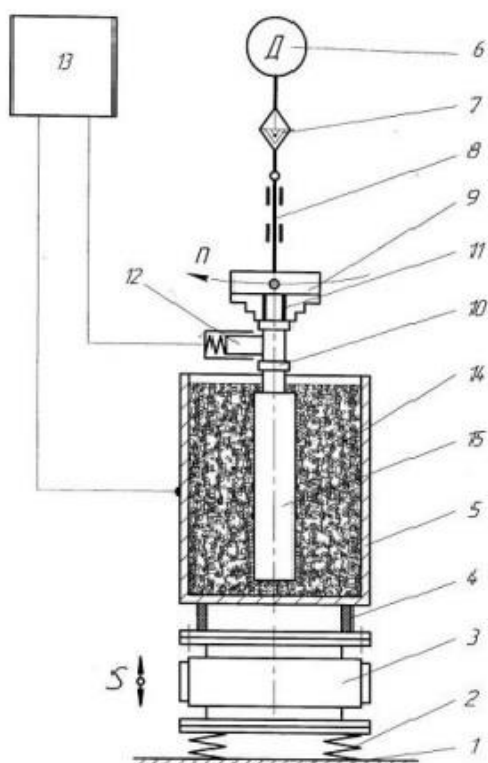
Схема установки для віброелектроіскрової обробки поверхонь деталей перед газотермічним напильненням покриттів [21]
